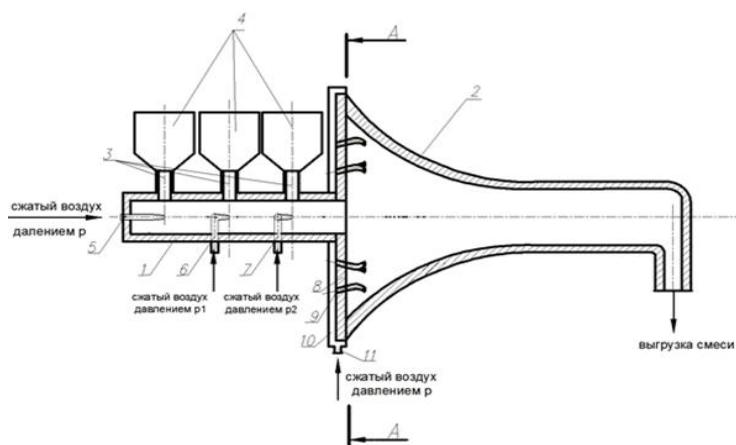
Пневмосмеситель непрерывного действия: 1 – подающая труба; 2 – корпус основной камеры смешения; 3 – патрубки ввода компонентов; 4 – загрузочные бункера; 5, 6, 7 – сопла дополнительные; 8 – торец; 9 – сопла; 10 – крышка; 11 – патрубок подвода сжатого воздуха
